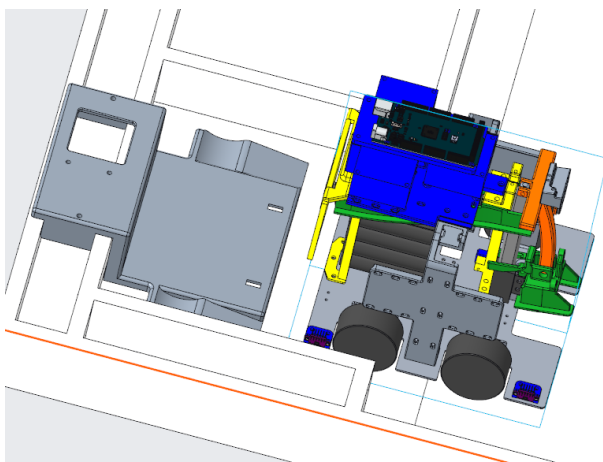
EcoDrop3 mit Ladestation und Aussenhülle
